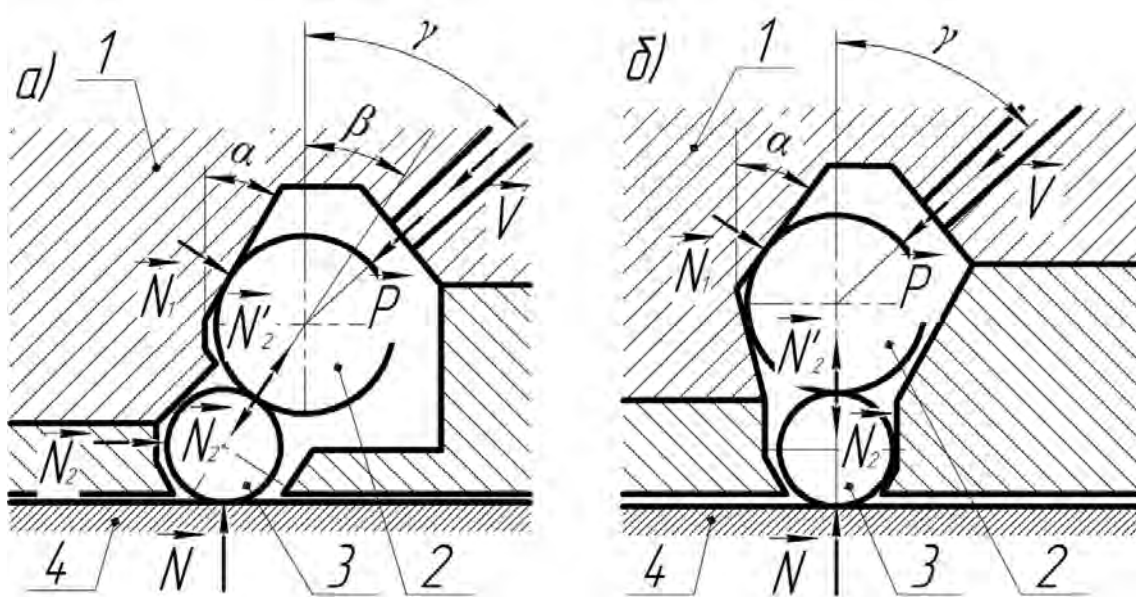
Схемы воздействия сил на шары инструмента и обрабатываемую поверхность: а –  $\beta \neq 0$ , б –  $\beta = 0$ ; 1 – направляющая поверхность; 2 – шар-ударник; 3 – боек (шар); 4 – обрабатываемая поверхность
